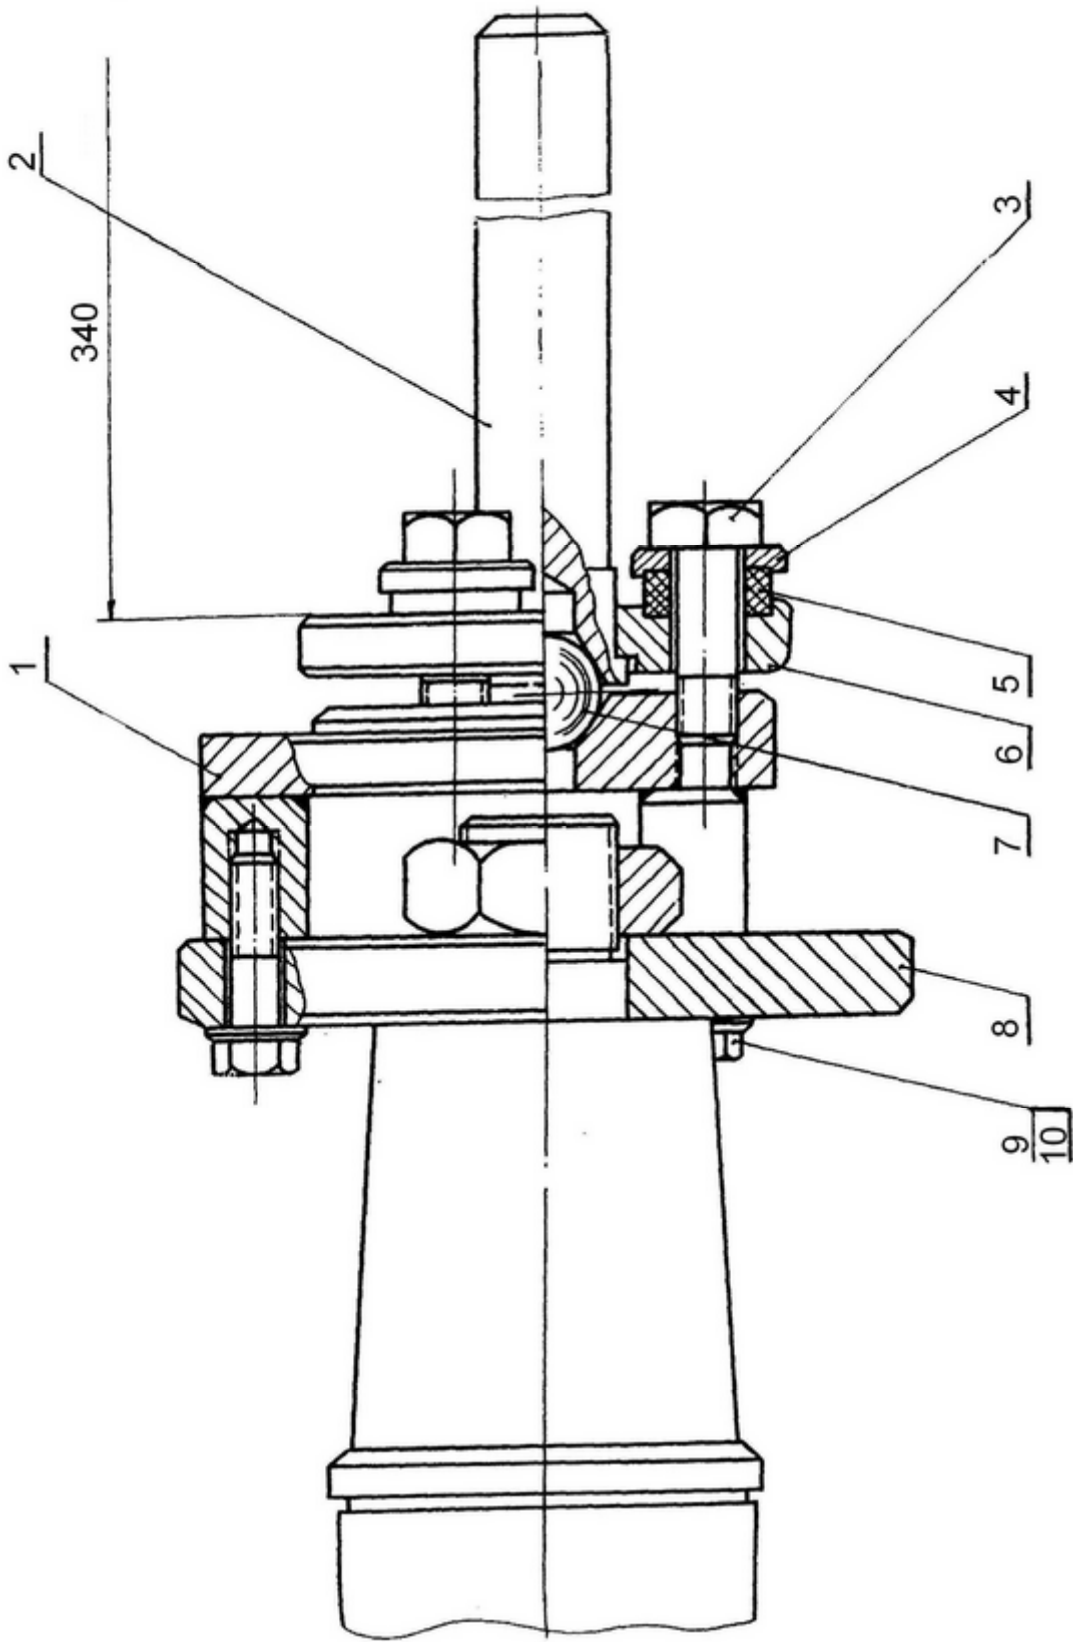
Регулируемая оправка для проверки на точность круглошлифовальных станков
